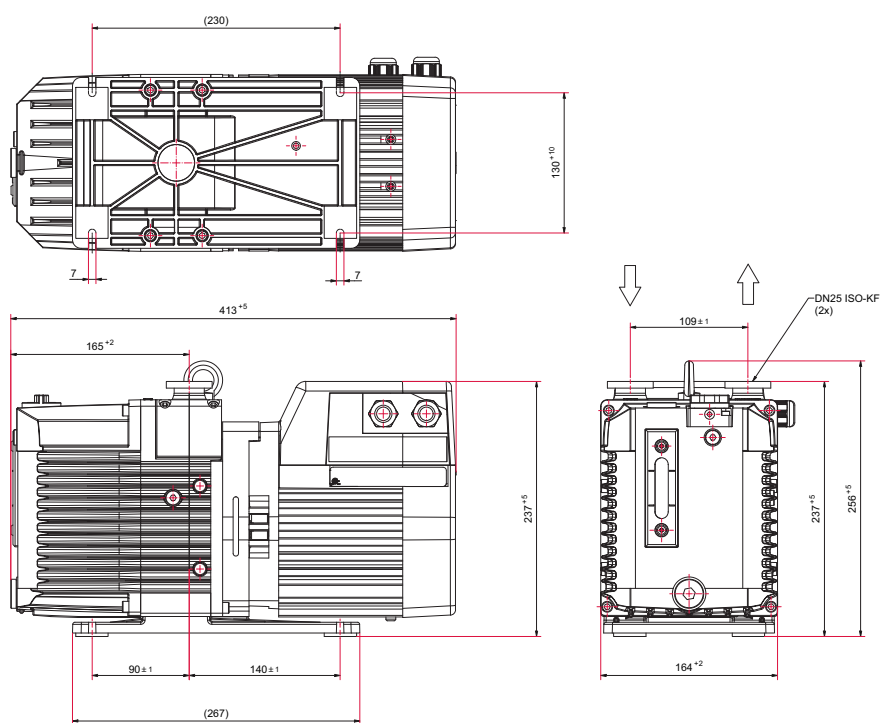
Dimensions DuoVane 6 avec moteur triphasé
